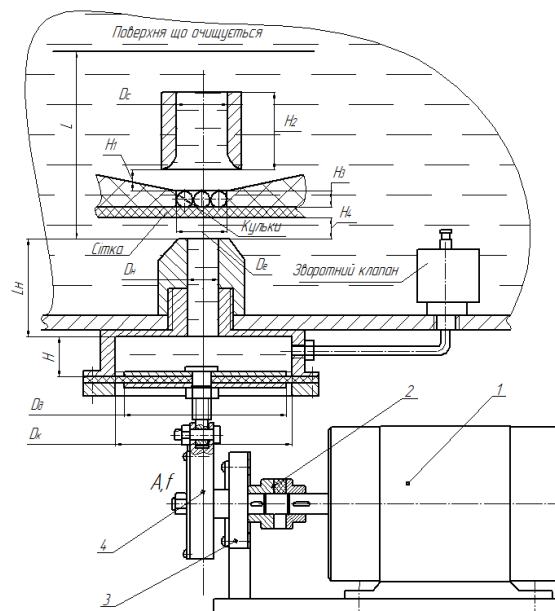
Розрахункова схема модуля вібраційної машини для очистки забруднень потоком пульсуючого струменя рідини з твердими частинками: 1 – електродвигун; 2 – муфта; 3 – корпус з підшипником; 4 – обойма ексцентрика з підшипником;  $H$  – висота камери пульсації;  $D_e$  – діаметр ежектора;  $D_c$  – діаметр сопла;  $H_1$  – відстань від сопла до ежектора;  $H_2$  – довжина сопла;  $H_3$  – висота кармана ежектора;  $H_4$  – відстань від зрізу насадка до сітки ежектора
